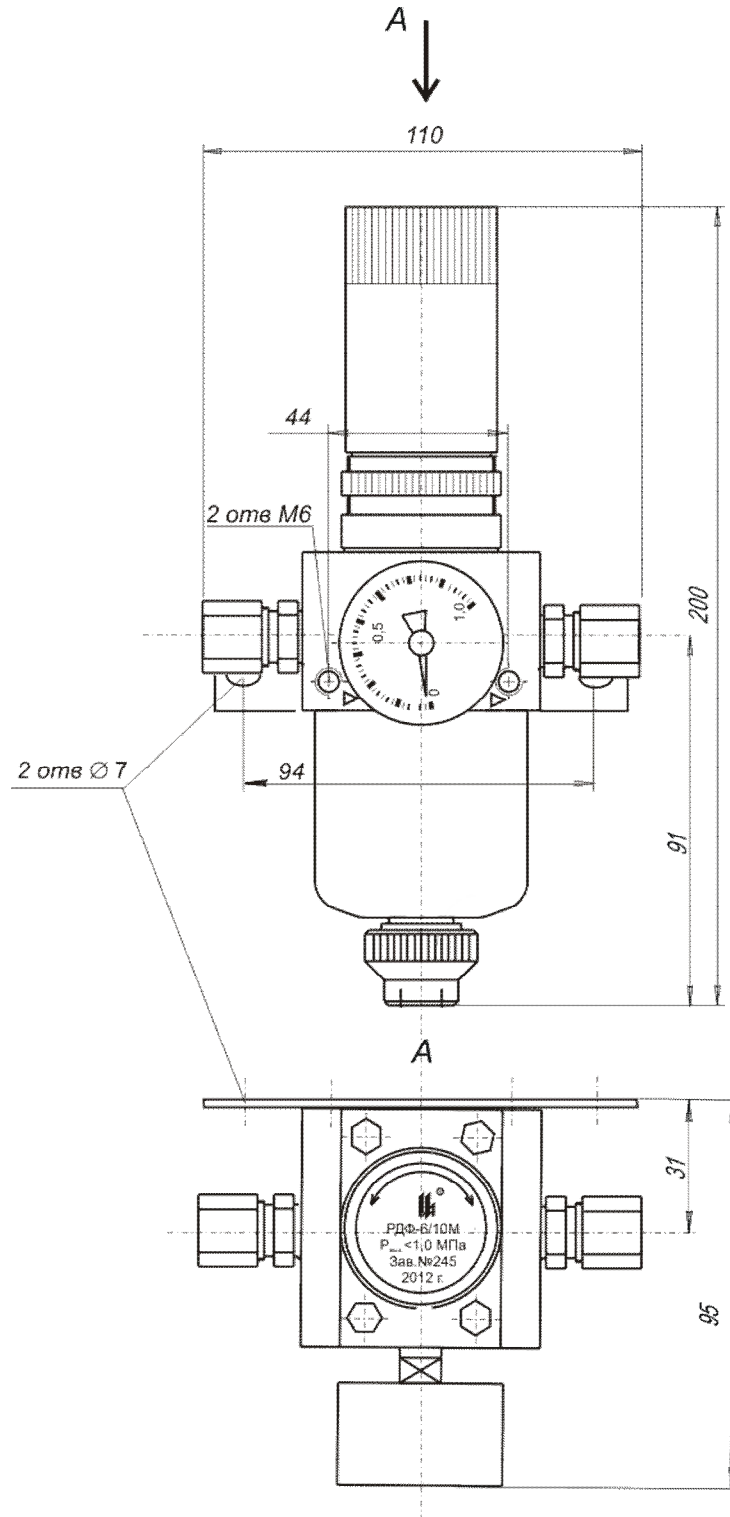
Габаритные и присоединительные размеры редуктора РДФ-6/10М
